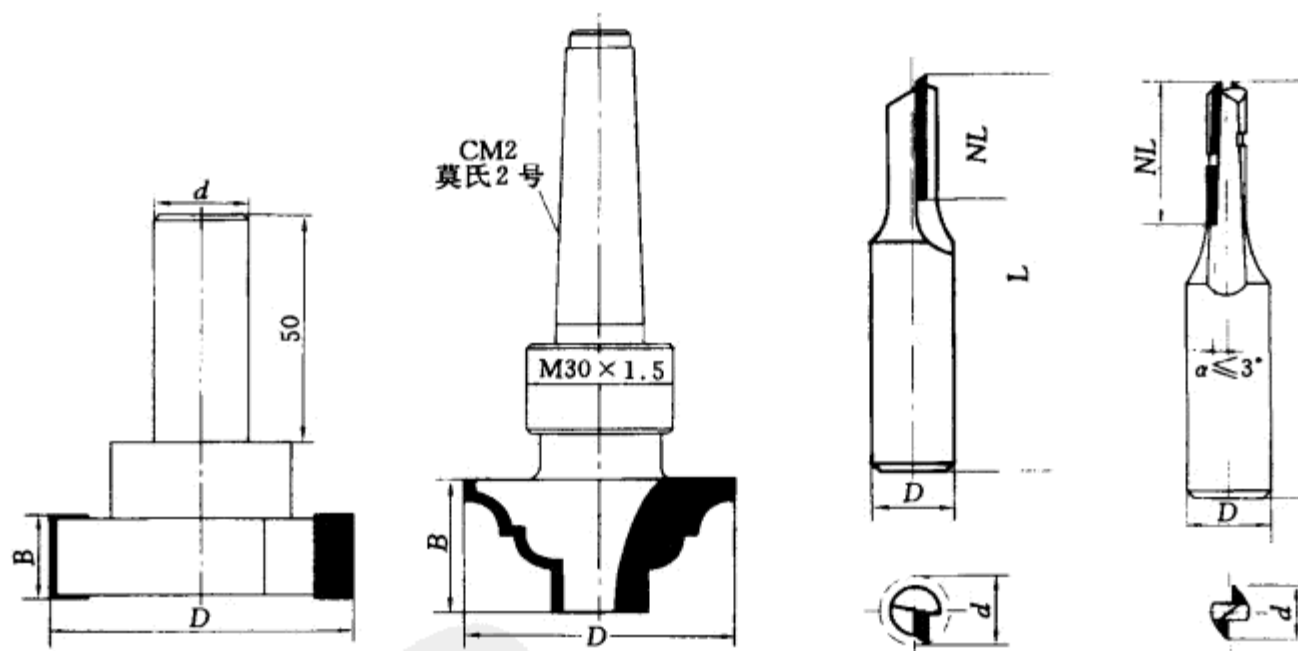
焊接硬质合金刀片柄的铣刀
